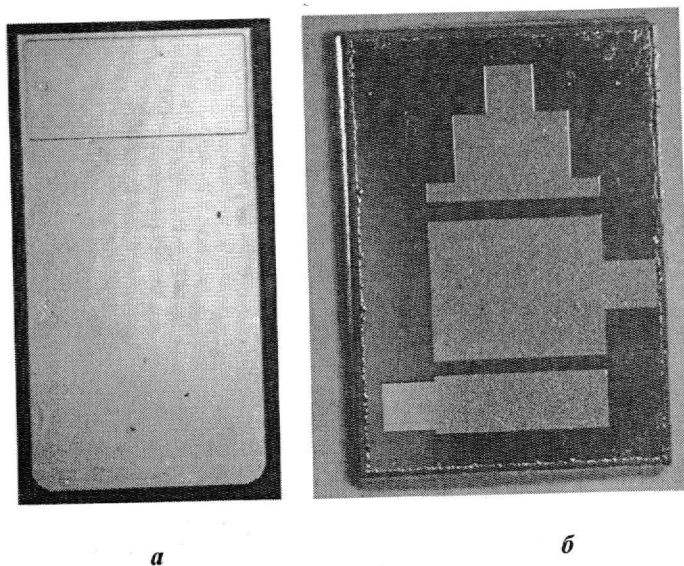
Детали микромеханического реле: а – якорь (лицевая сторона); б – статор
